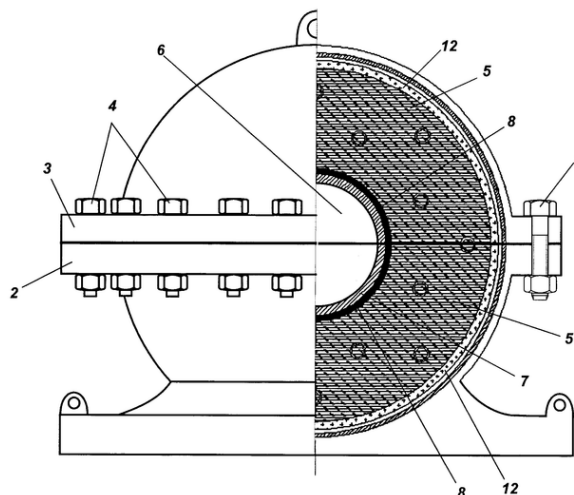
Вариант взрывной камеры патента 2619545 [3]: 2 - дно цилиндра, 3 – крышка цилиндра, 4- резьбовые соединения, 5 – силовой элемент, 6-рабочая полость, 7- рабочая поверхность, 8 - компенсационная прокладка, 12 - гидравлическая камера
